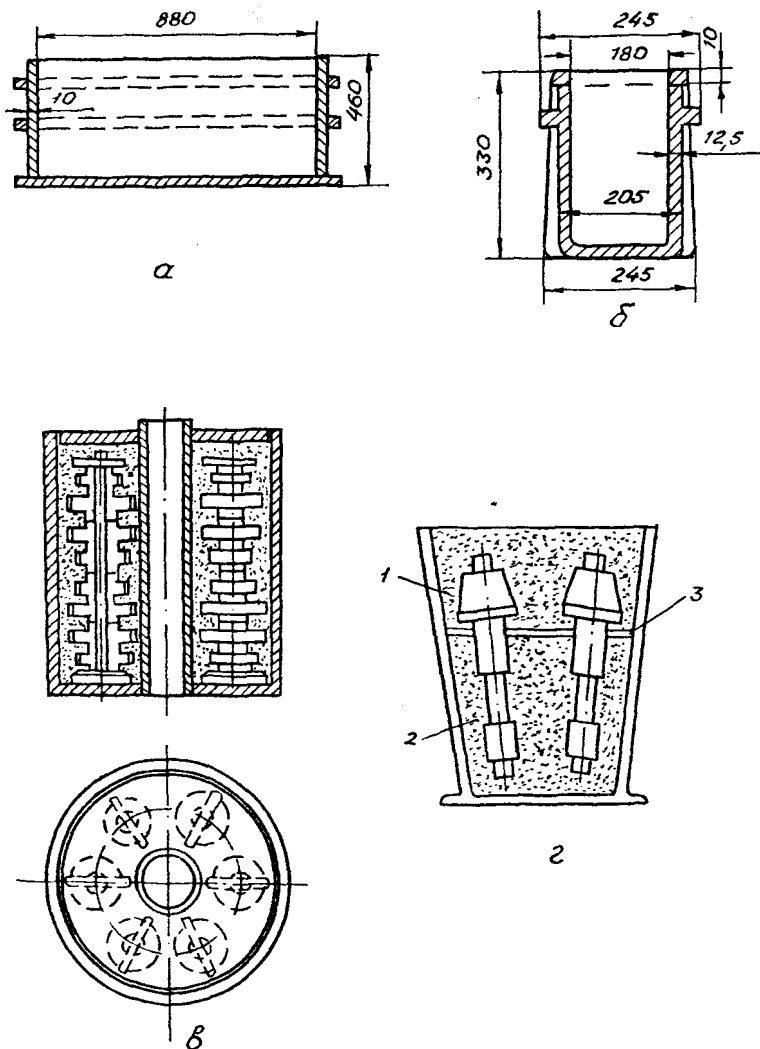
Ящики для цементации твердым карбуризатором: а — призматические стальные сварные; б — чугунные литые; в — цилиндрические с внутренней трубой; г — цилиндрические для цементации части детали: 1 — карбуризатор; 2 — песок; 3 — прокладка
